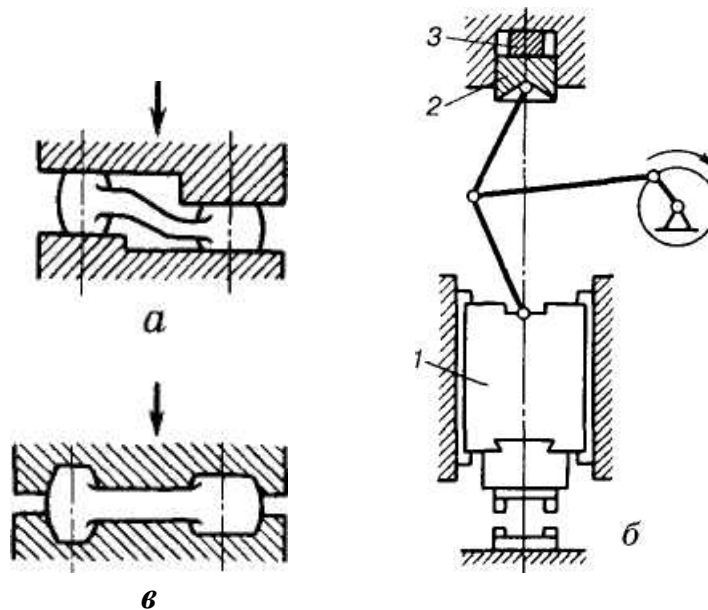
Схеми калібрування і кривошипно-колінного преса
